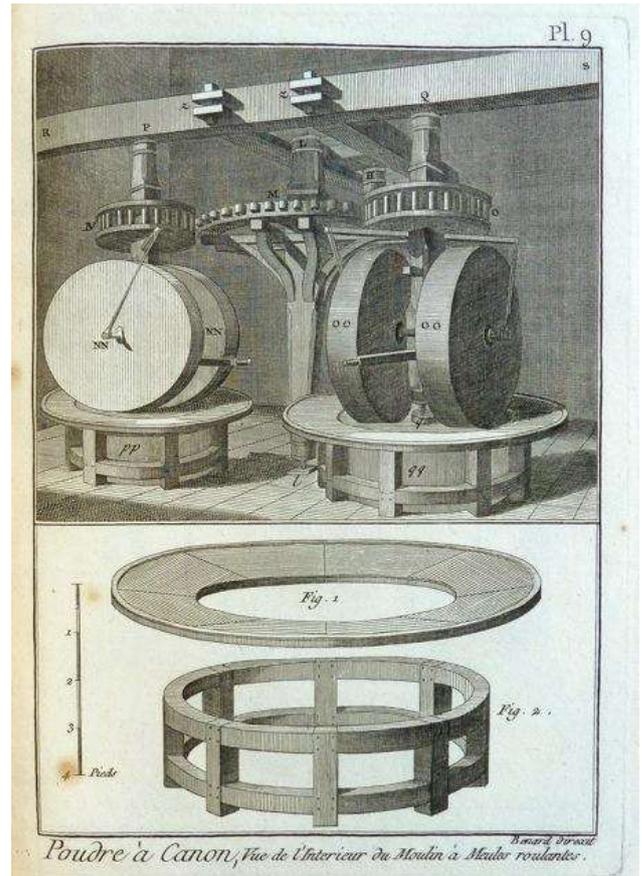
Walzmühle mit Bodenplatte und Läufer (Diderot, Encyclopédie, Poudre à canon, Planche 9)
